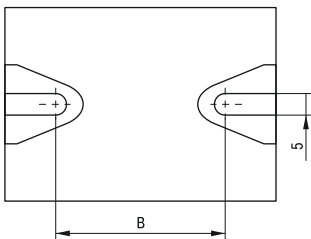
Установочные размеры шин / Figure 3 – Busbar mounting dimensions
